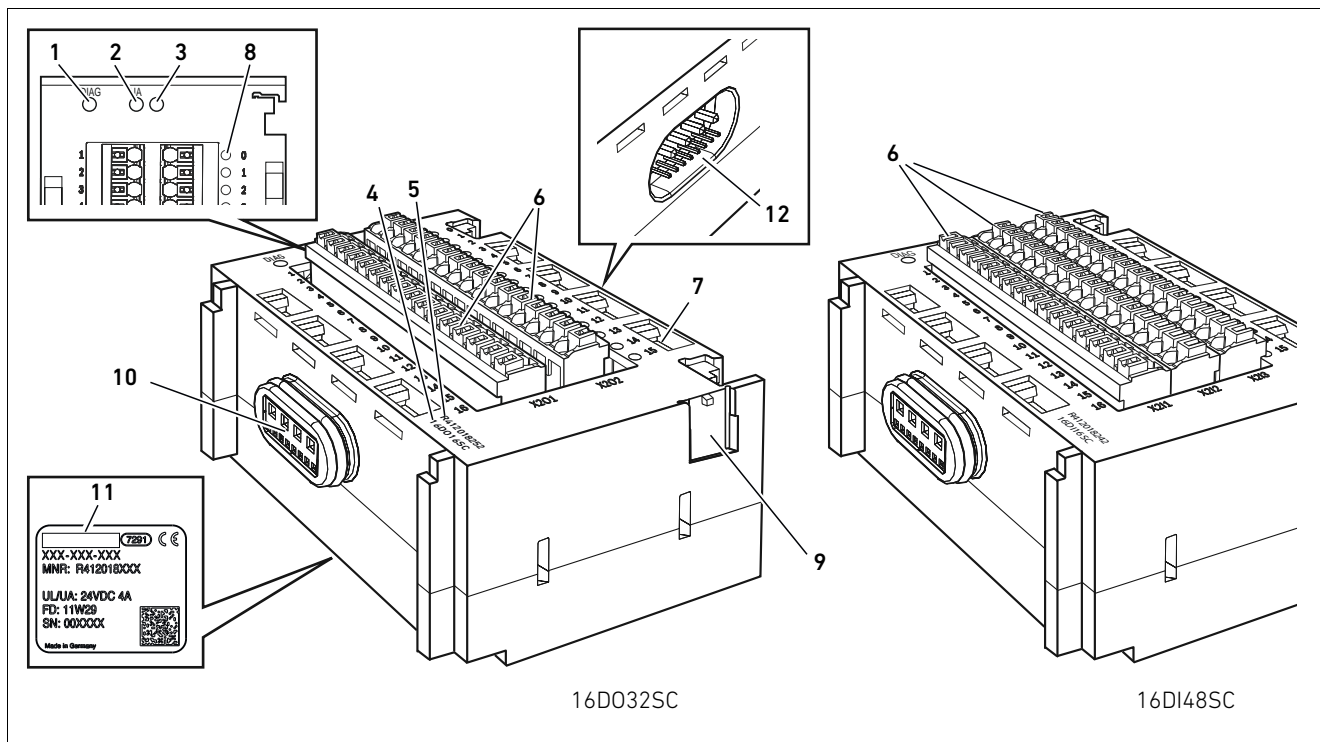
Vue d'ensemble du module de sortie 16D032SC et du module d'entrée 16DI48SC
